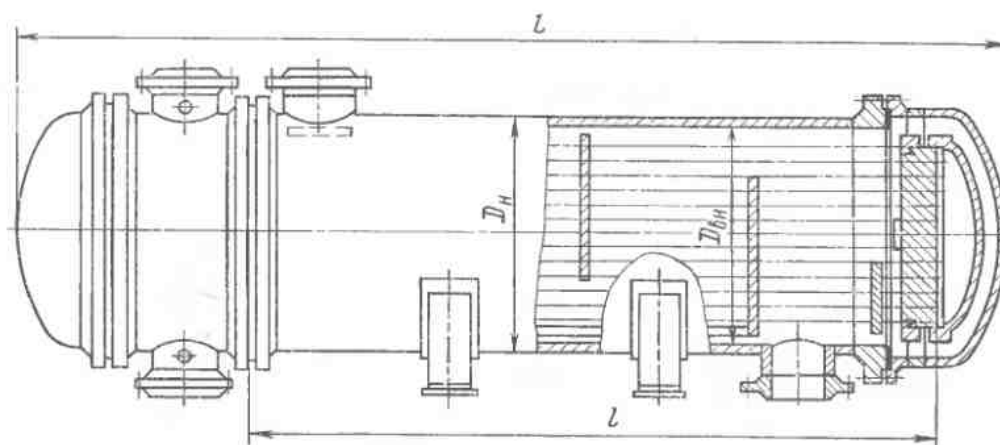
Кожухотрубчатый горизонтальный многоходовой теплообменник с плавающей головкой
